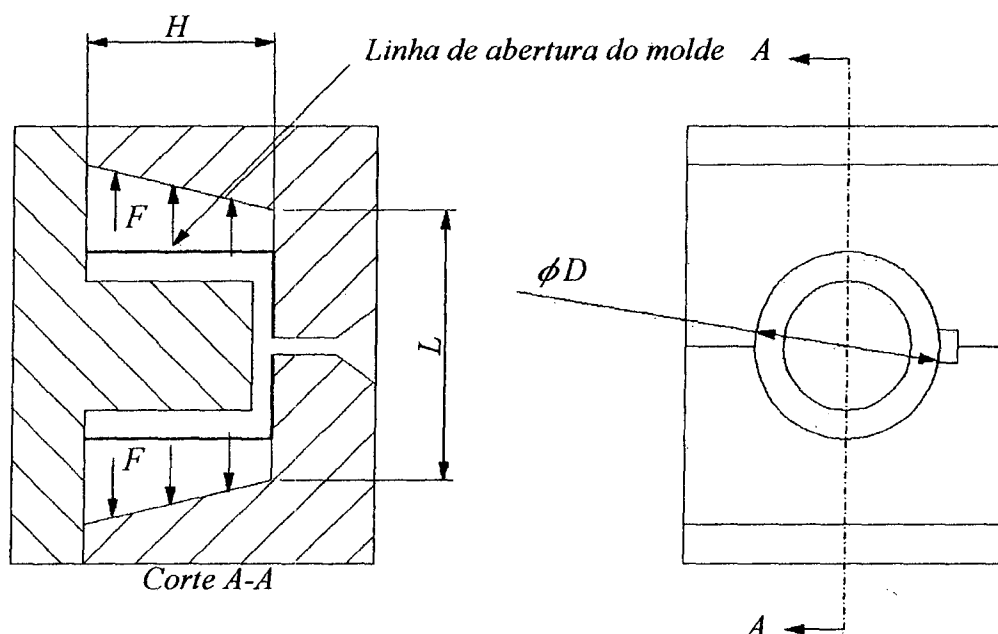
Molde com gavetas em cunha – primeiro princípio de solução
